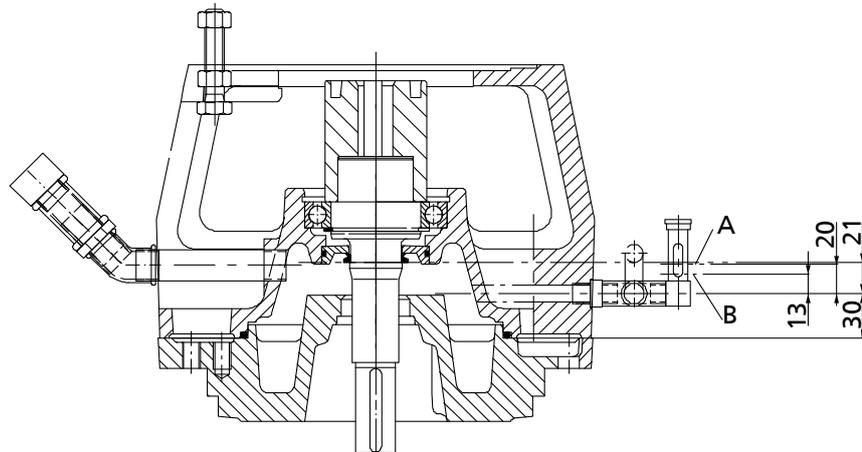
Riempimento della precamera dell'olio - Installazione verticale
